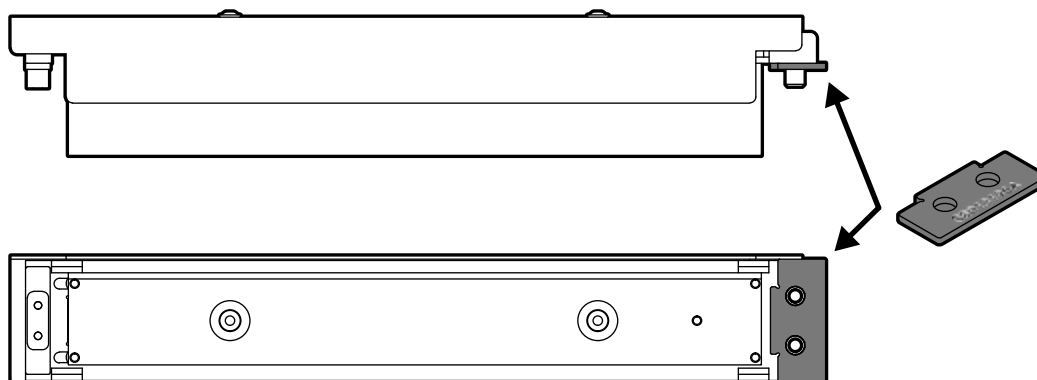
Prawidłowy odstęp między Recoater blade a komorą druku.
